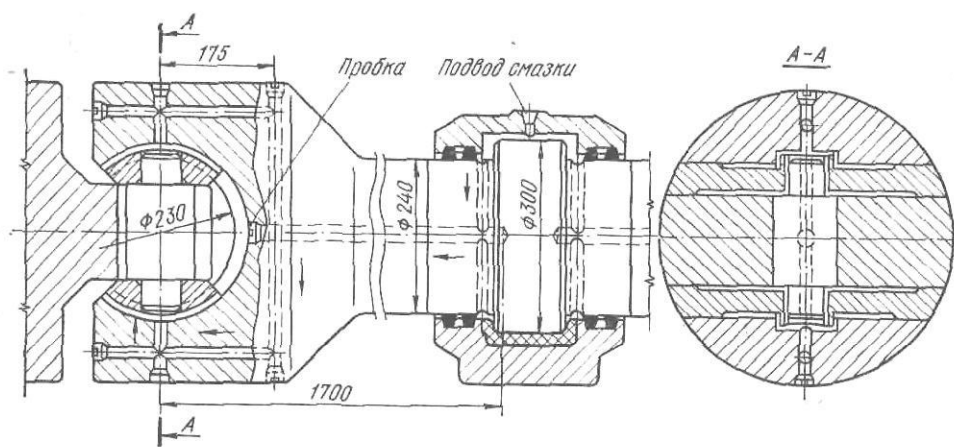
Универсальный шпindelь привода валков четырехвалковой клетки стана 1700
